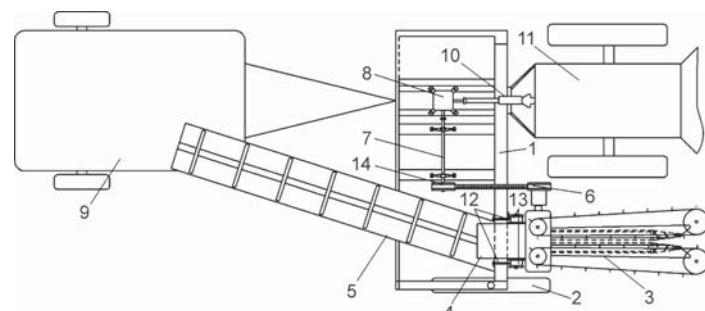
Схема кукурузоуборочного комбайна (вид сверху):
